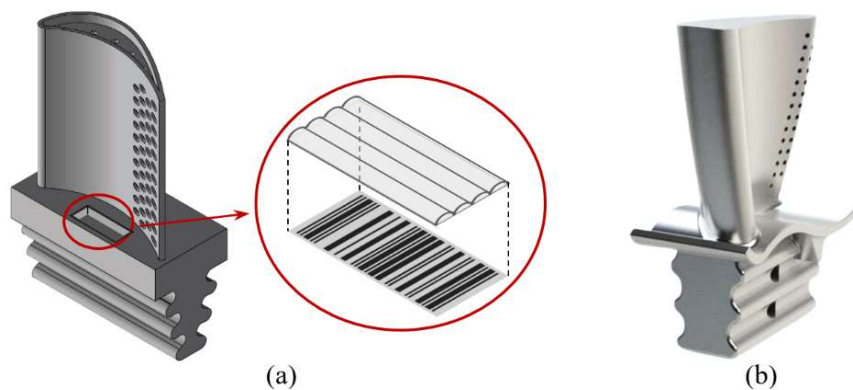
(a) Diseño CAD de la pieza de alto valor añadido preparada para la impresión y recubrimiento de un identificador mediante DED-LB y (b) pieza final tras el proceso de impresión e operaciones de acabado.
